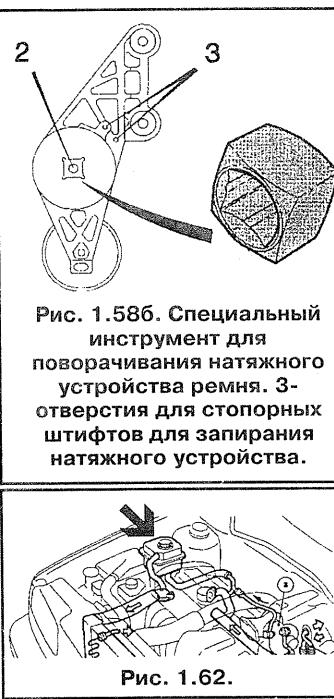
Специальный инструмент для поворачивания натяжного устройства ремня. 3- отверстия для стопорных штифтов для запирания натяжного устройства.
